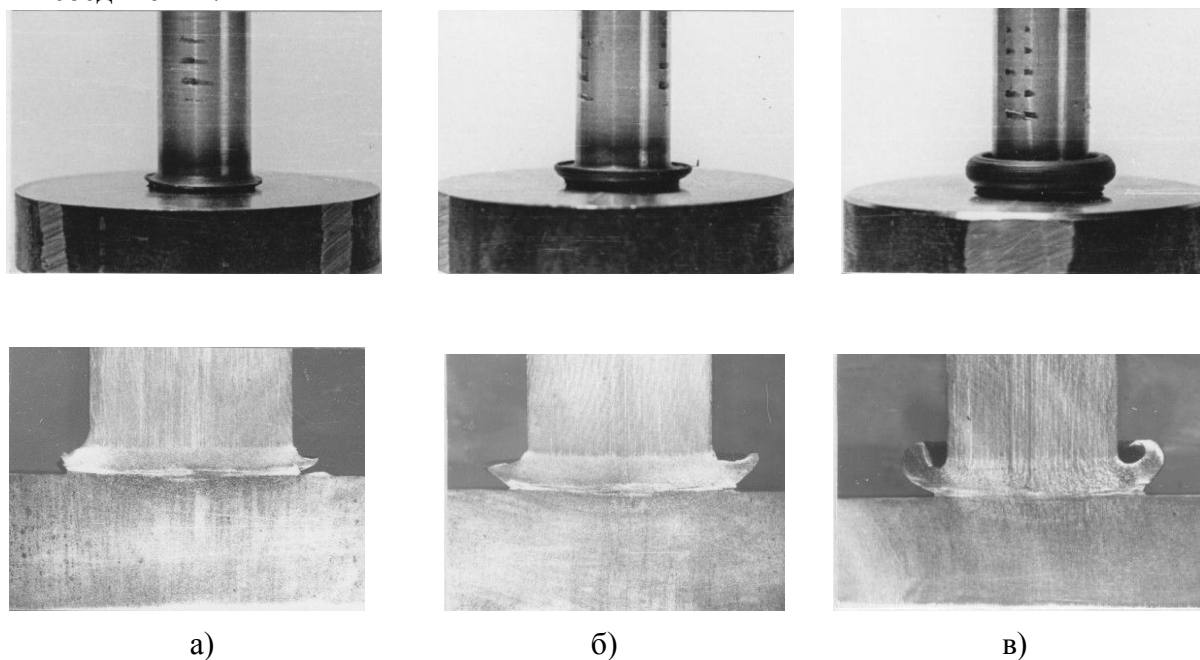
Внешний вид и макроструктура сварных соединений, полученных с различной длительностью времени нагрева:
